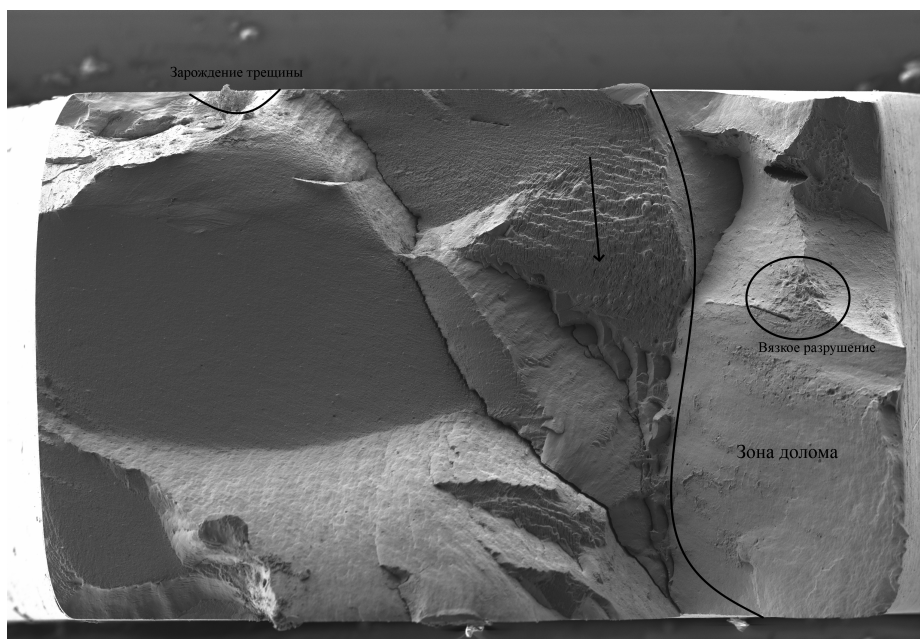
Поверхность разрушения УМЗ образца Al 6101
